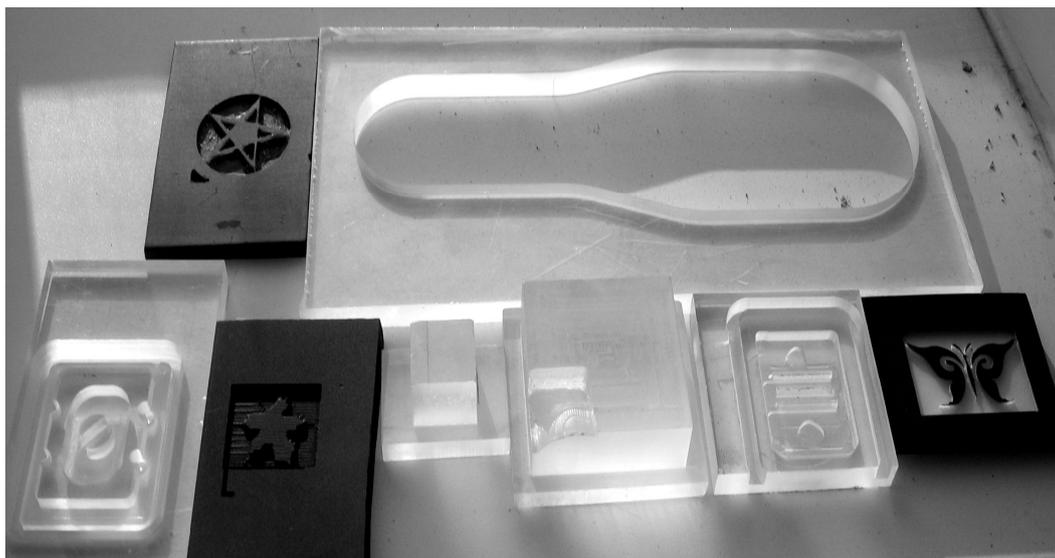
Образцы деталей, изготовленных на фрезерных станках с компьютерным управлением
